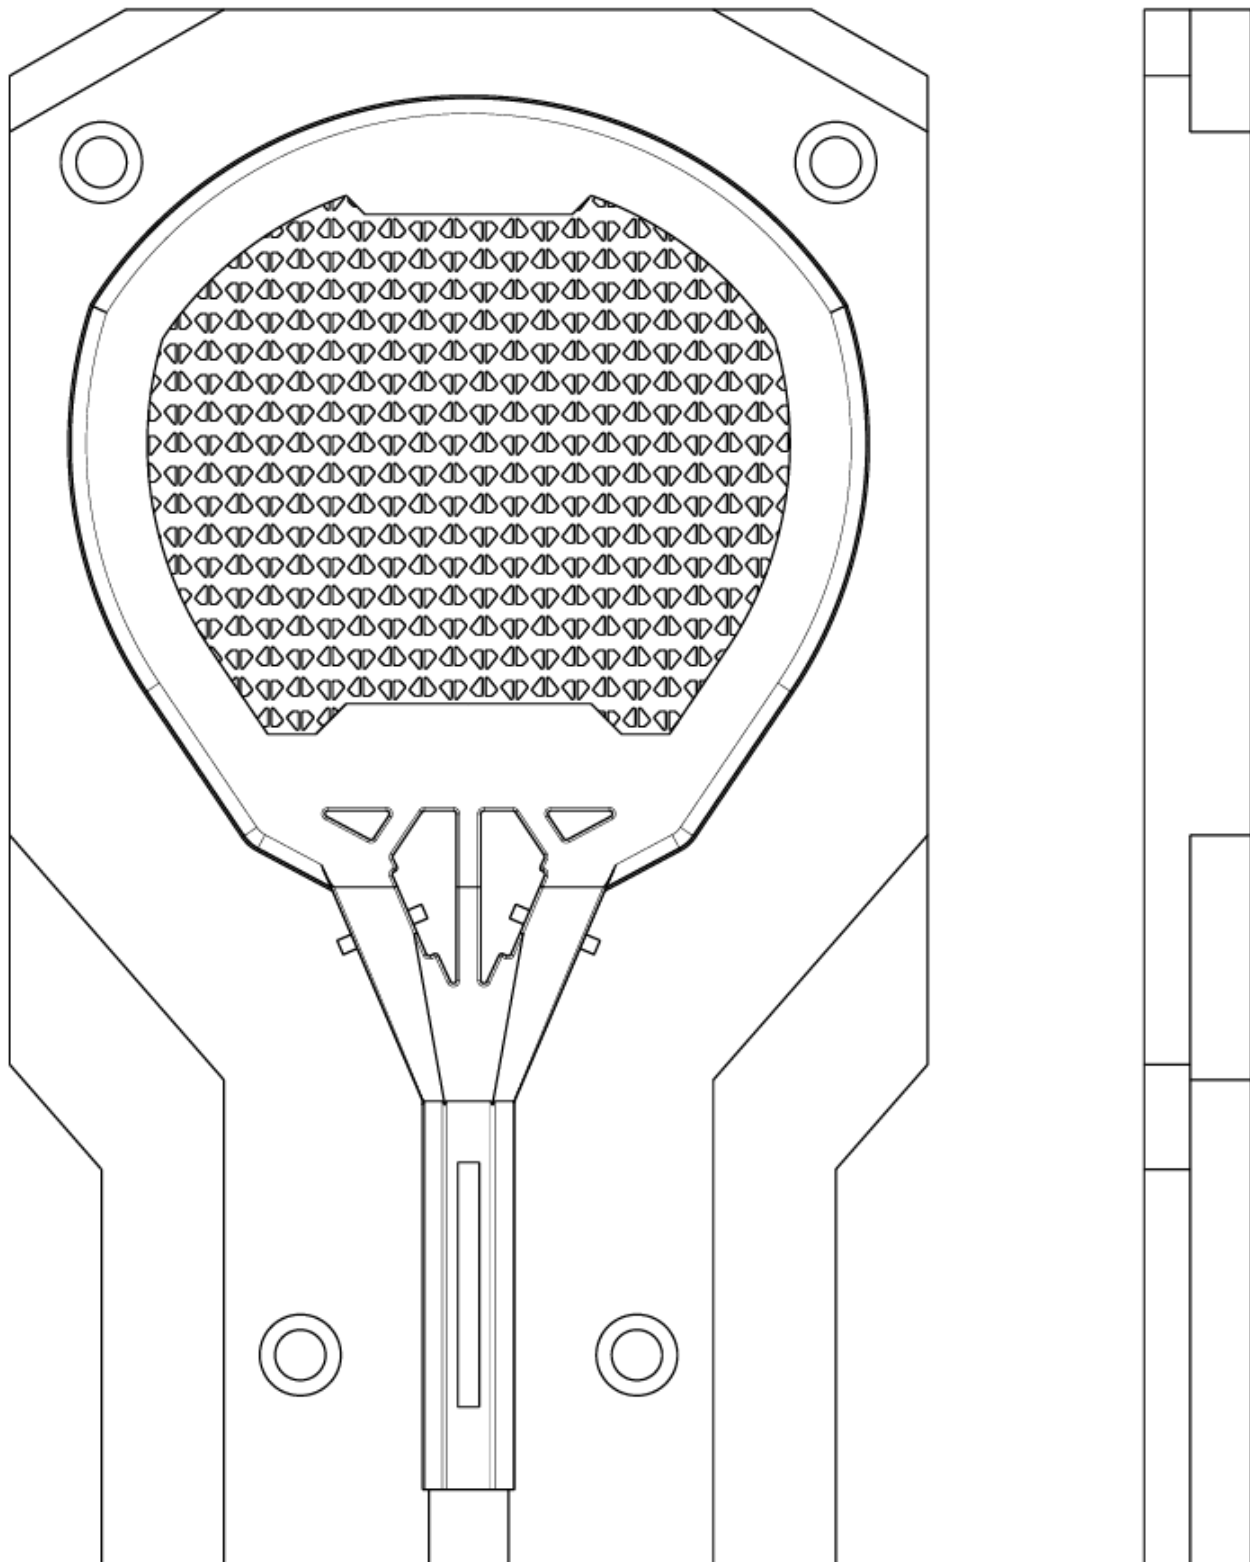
Alzado y perfil derecho del diseño propuesto para la placa inferior del molde.
